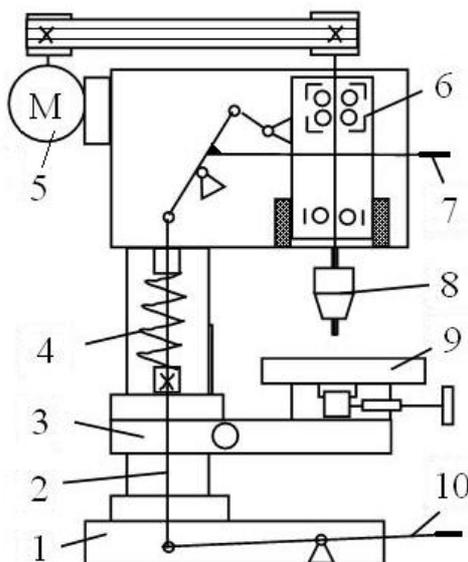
Схема станка сверлильно-фрезерного СВП-2:
